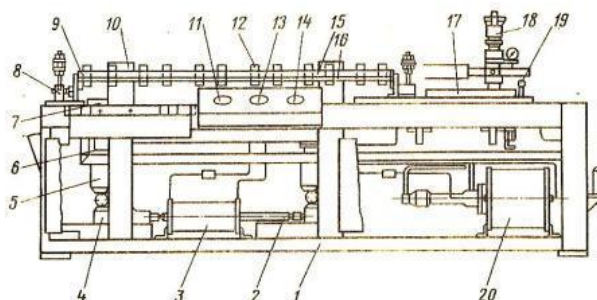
Стенд для ремонта молотильных барабанов: 5) – Механизм подъёма/опускания; 8) – Ограничительные упоры с роликами; 11) – Кран управления; 13) – Кран управления; 14) – Кран управления; 15) – Установочная линейка; 16) – Установочная линейка.
